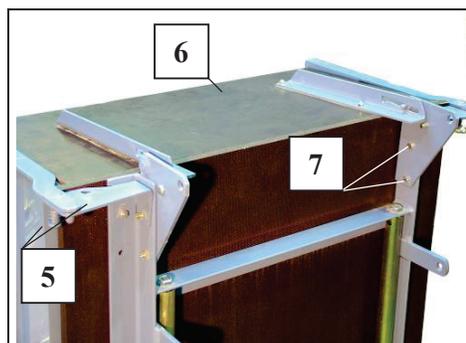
Монтаж бортовой стенки комбинируемой платформы
